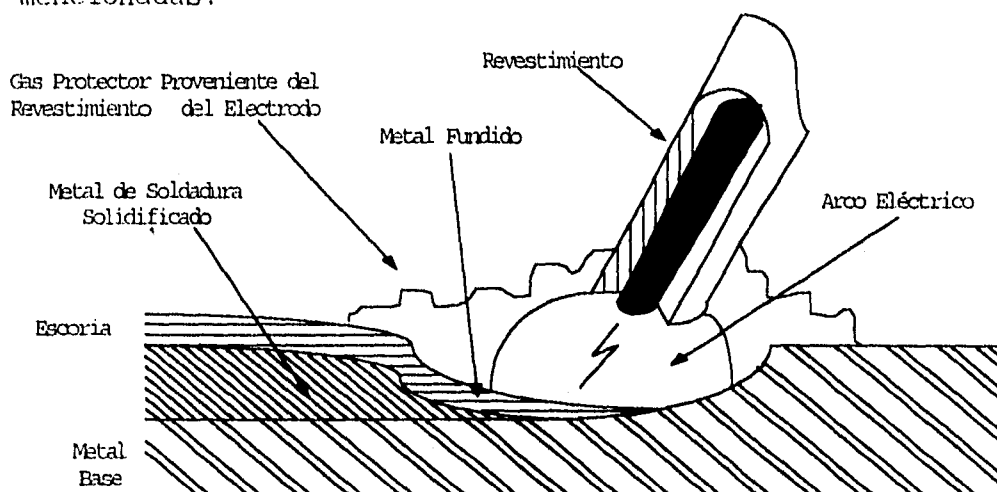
Diagrama esquemático del proceso de soldadura por arco eléctrico con electrodo.
